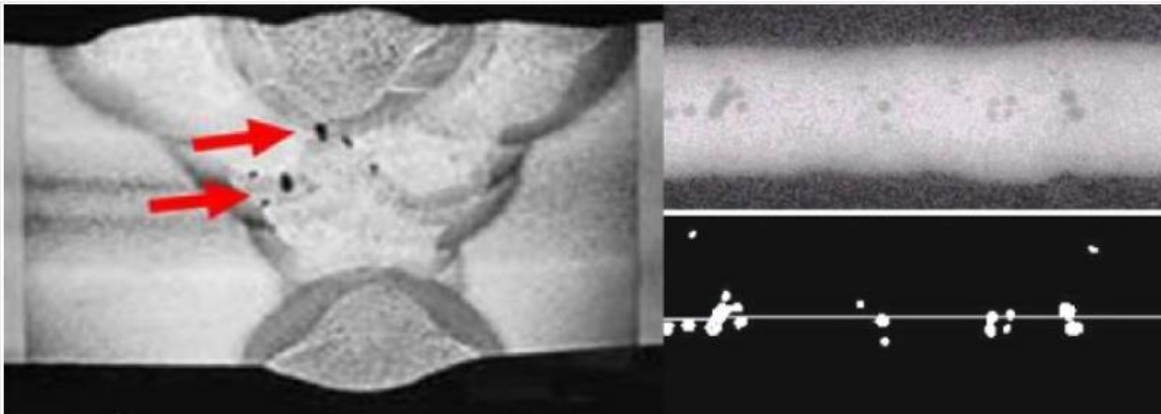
Ejemplos de porosidades en soldaduras, vistas en superficie y en sección.
